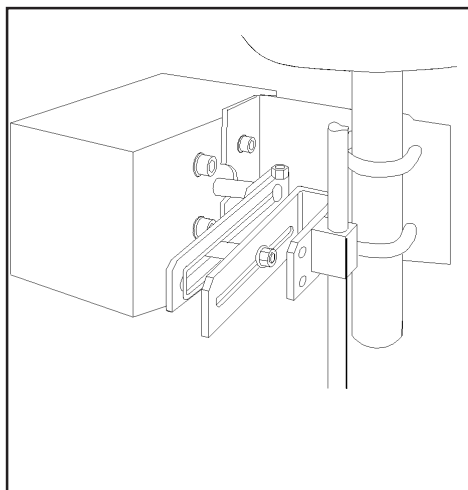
Montagem de um atuador de haste (IEC 534 parte 6)
